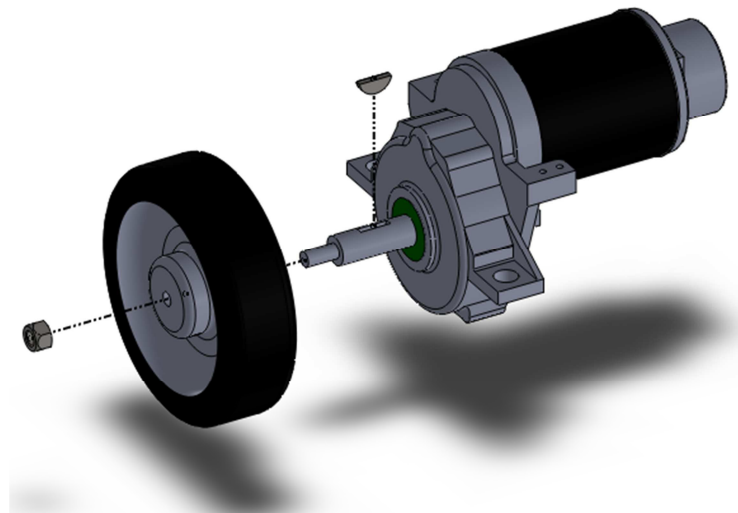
Vista explosionada del montaje de la llanta delantera.
